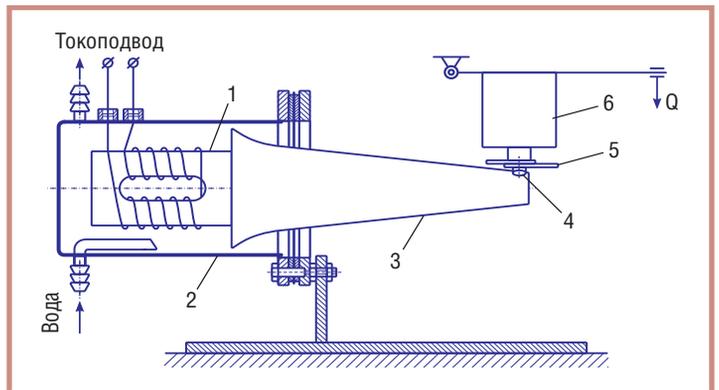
Схема установки для точечной сварки ультразвуком: 1 — электромеханический преобразователь; 2 — металлический корпус; 3 — трансформатор упругих колебаний; 4 — сварочный наконечник; 5 — свариваемые детали; 6 — прижимная опора;
